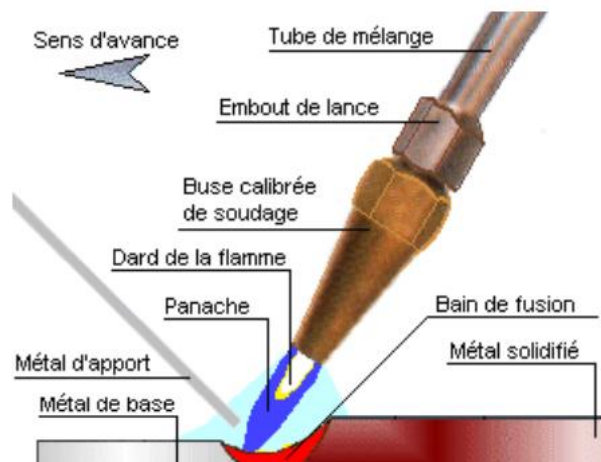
Soudage oxyacétylénique. [21]
